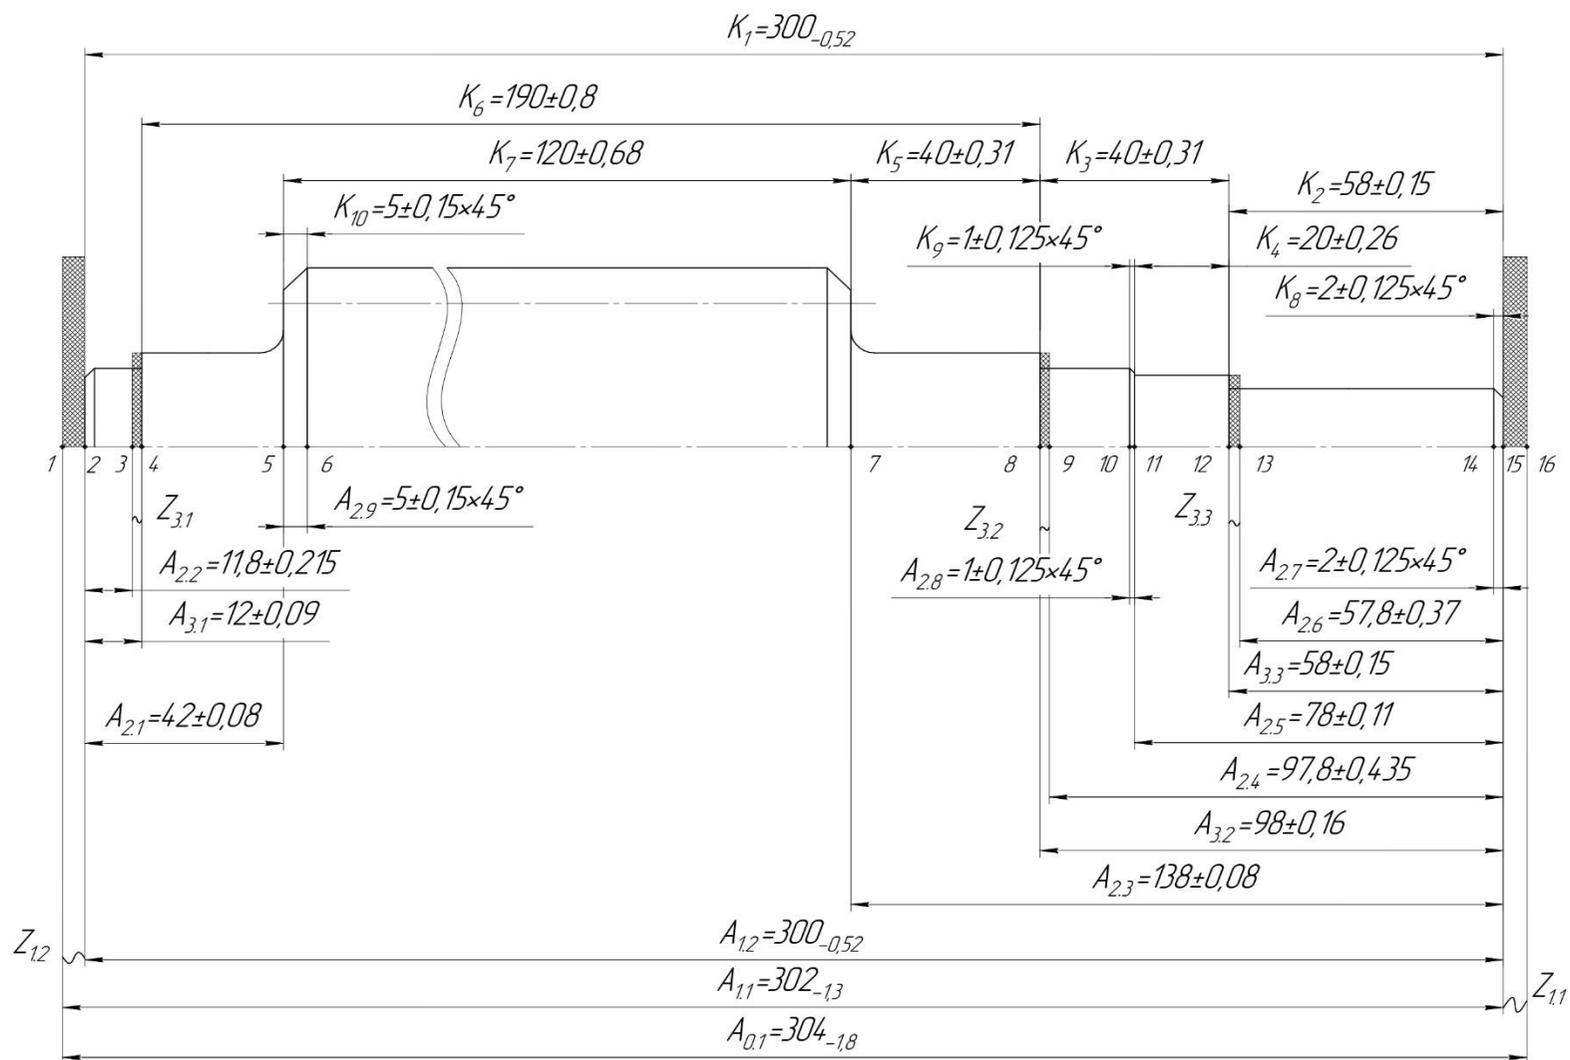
Размерная схема технологического процесса изготовления «Червяка цилиндрического»
